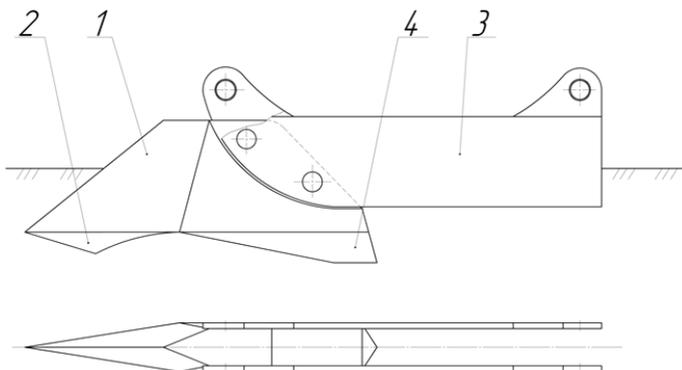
Патент UA 133540: 1 – верхня робоча поверхня; 2 – нижня робоча поверхня; 3 – щоки; 4 – п’ята
